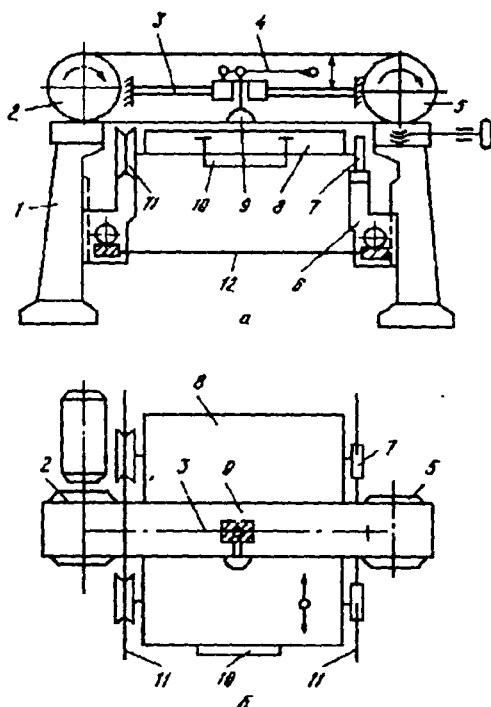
Функциональная схема одноленточного шлифовального станка ШЛПС-5 с ручной подачей деталей:
